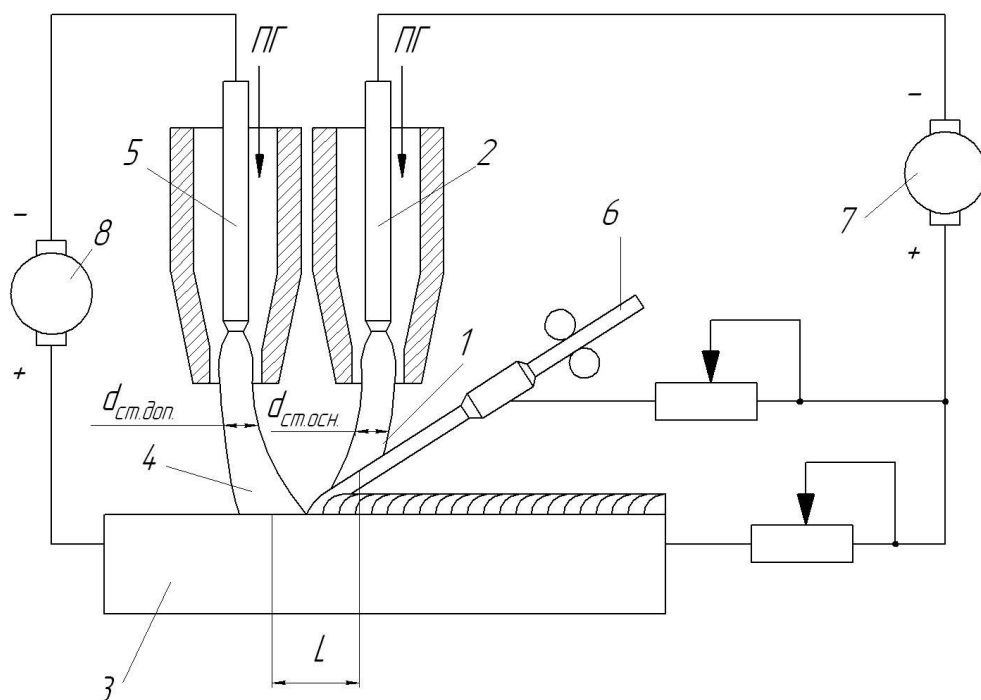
Схема предлагаемого способа плазменной наплавки
